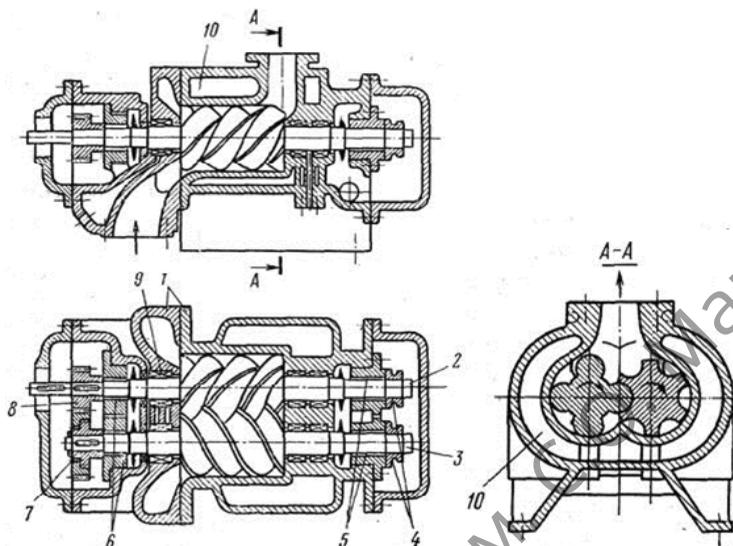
Винтовой компрессор с охлаждаемым корпусом:
